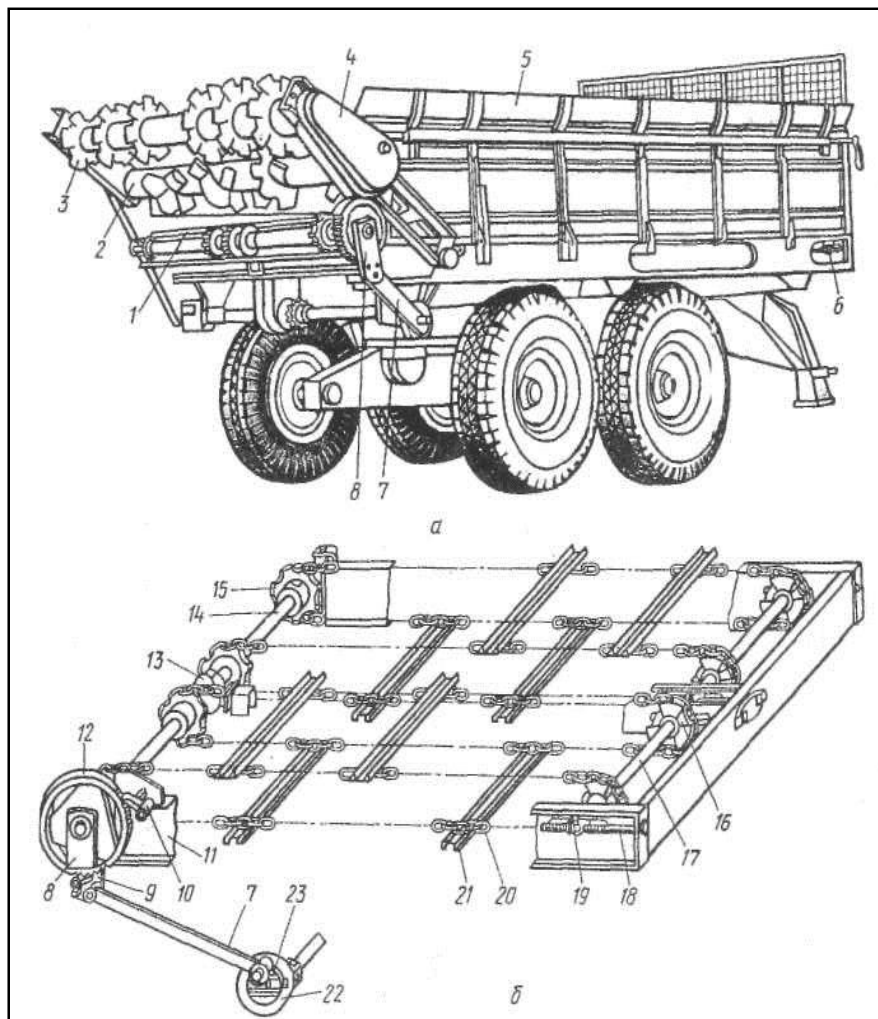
Машина для внесения органических удобрений РОУ-6М: а – общий вид; б – транспортер; 1 – цепочно-планчатый транспортер; 2 – измельчающий барабан; 3 – разбрасывающий барабан; 4 – защитный кожух передачи; 5 – надставной борт кузова; 6 – натяжное устройство; 7 – шатун; 8 – коромысло; 9 и 10 – ведущая и предохранительная собачки; 11 – брус рамы; 12 – храповое колесо; 13 – опорный подшипник; 14 и 17 – ведущий и ведомый валы; 15 – ведущая звездочка; 16 – ведомый ролик; 18 – натяжной болт; 19 – гайка; 20 – цепь; 21 – скребок; 22 – корпус кривошипа; 23 – диск кривошипа
